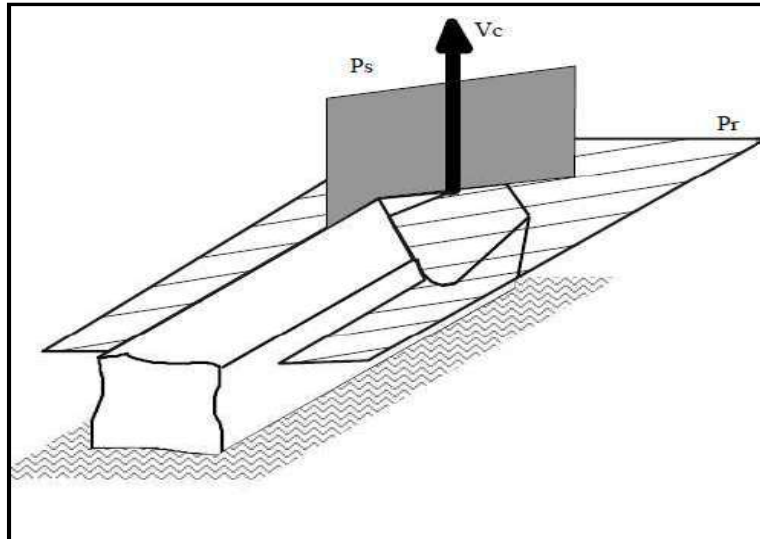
Plan de référence P_r et plan d'arête tranchante P_s
